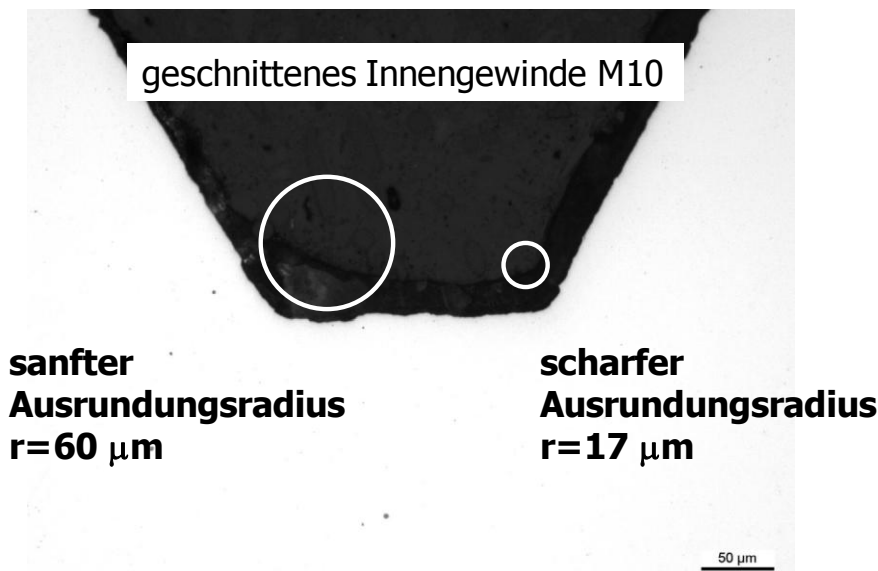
Gewindeausrundungsradius der Zugmutter
